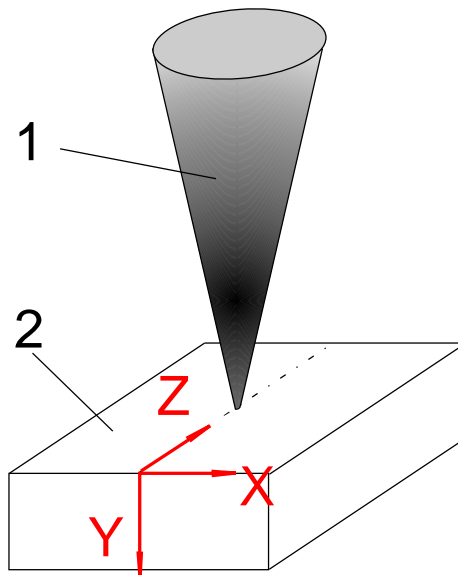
Прийнята система координат, де: 1-лазерний промінь; 2- заготовка.
